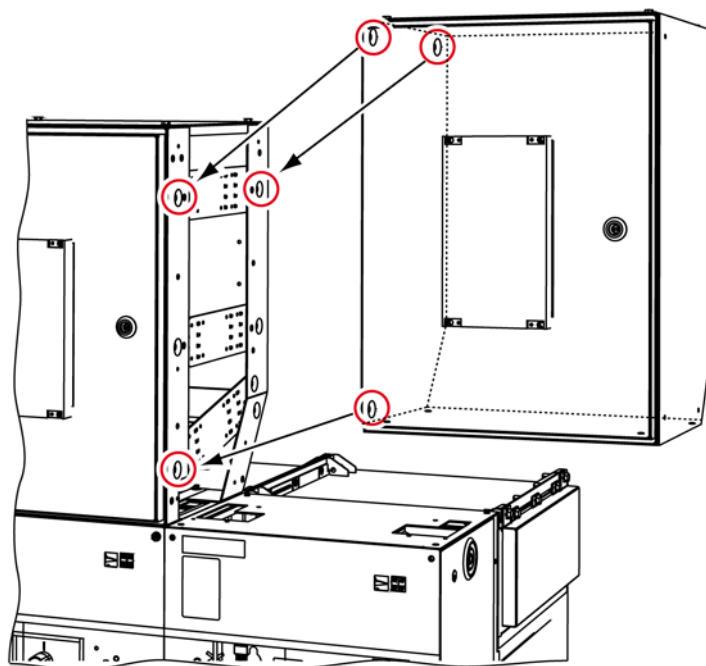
Крепление низковольтного блока к ячейке с помощью резьбовых соединений
